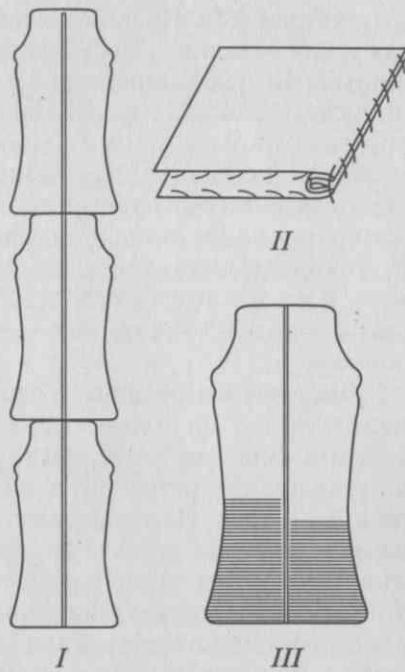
Этапы (I—III) изготовления боа из меха норки
